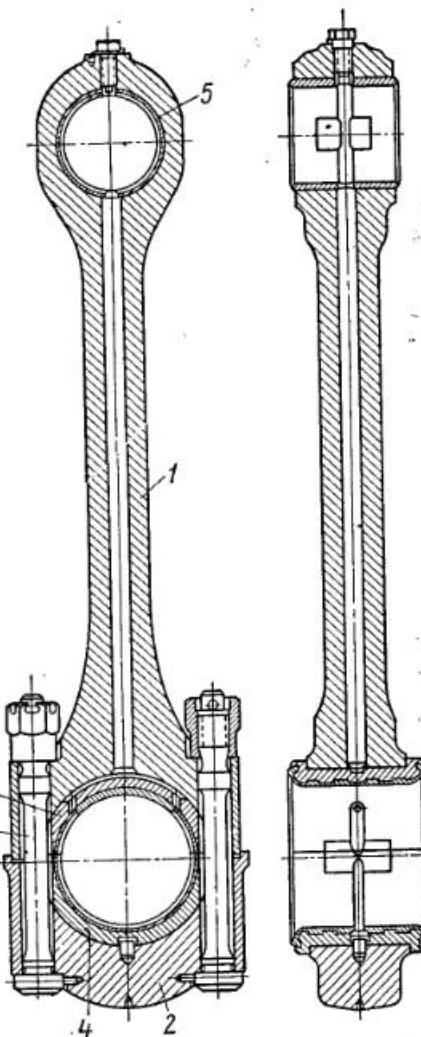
Шатун (в сборе) двигателей типа NVD-24:
